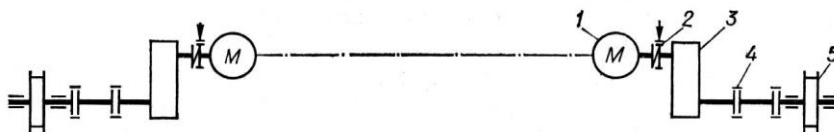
Кінематична схема механізму пересування конвеєра
